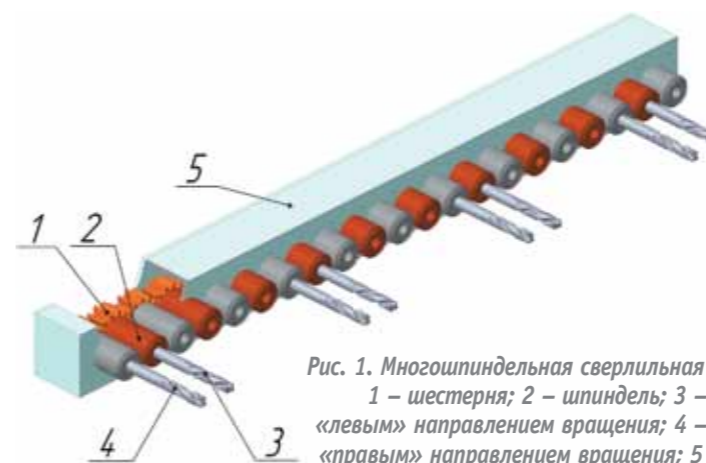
Многошпиндельная сверлильная головка. 1 – шестерня; 2 – шпindelь; 3 – сверло с «левым» направлением вращения; 4 – сверло с «правым» направлением вращения; 5 – корпус
